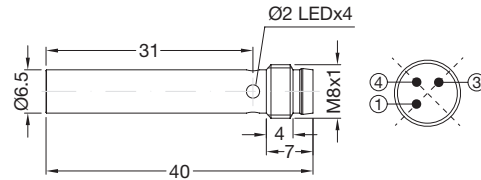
Kurze Ausführung, bündiger Einbau, Steckversion
